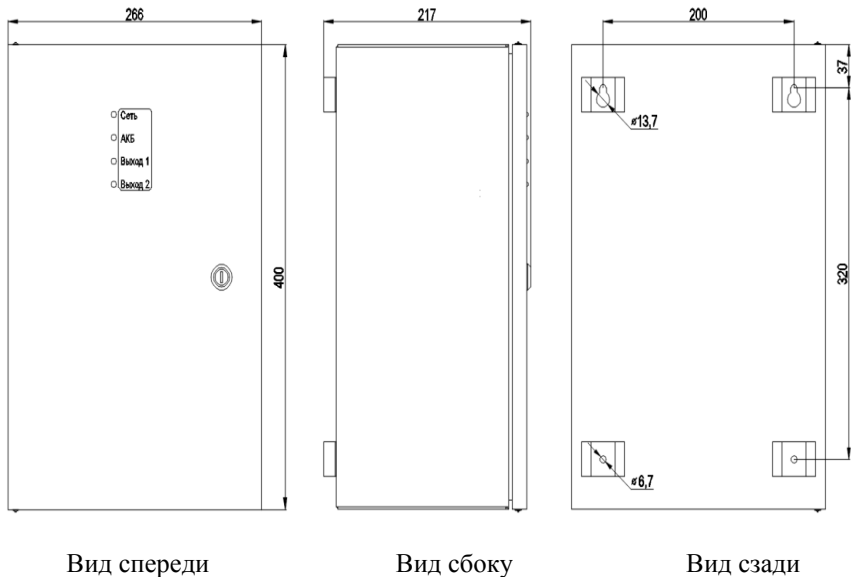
Внешний вид, габаритные и установочные размеры корпуса БПП
